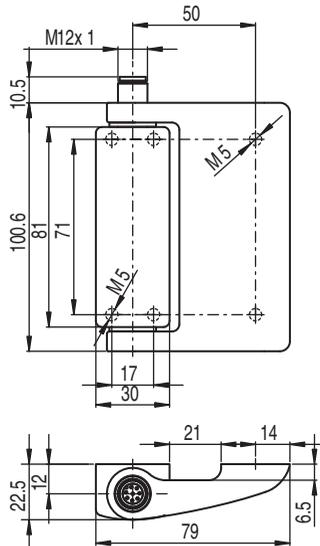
Dimensões do S410-M1M12-T em mm
